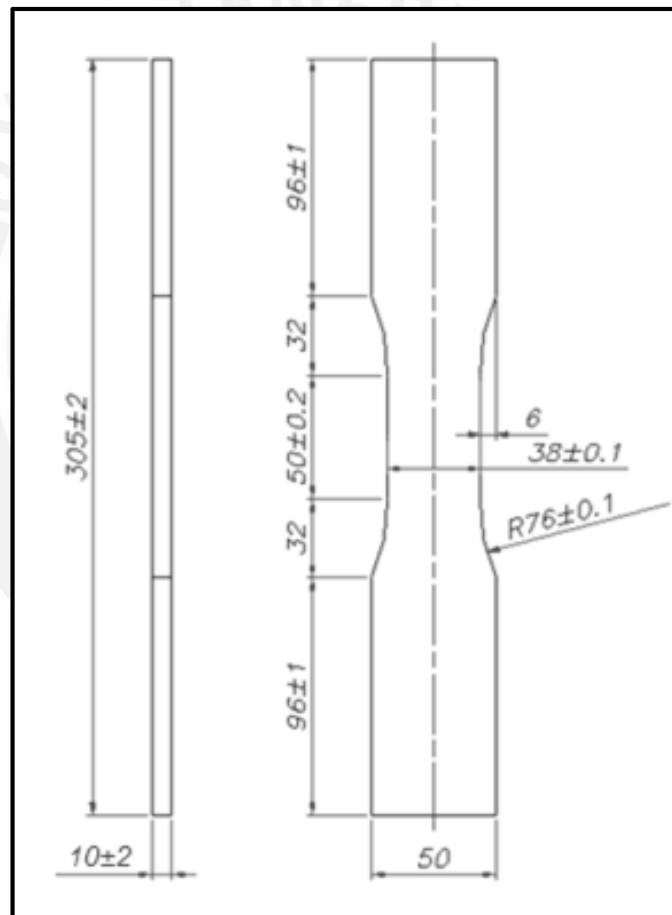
Dimensiones de la probeta de flexión según ASTM D 1037 – 06a
